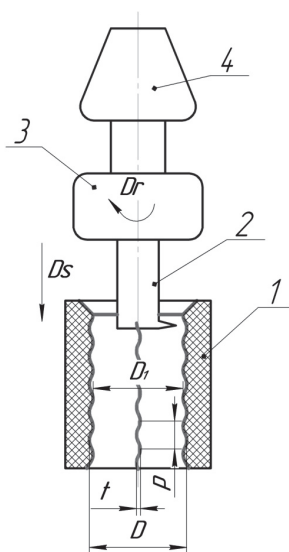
Схема фрезерування круглої різьби в АКМ
